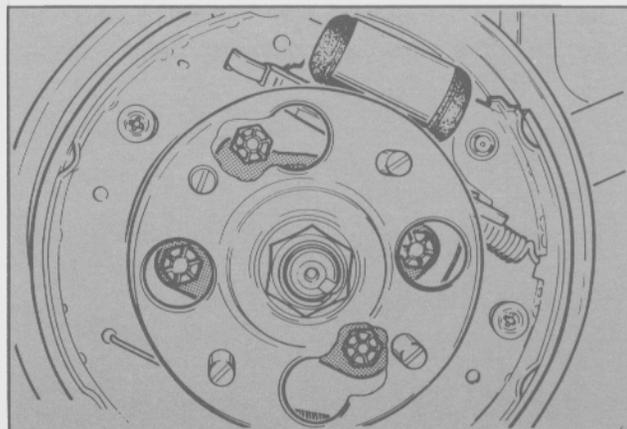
Montaje de la maza de rueda al brazo inferior (4 tornillos)
